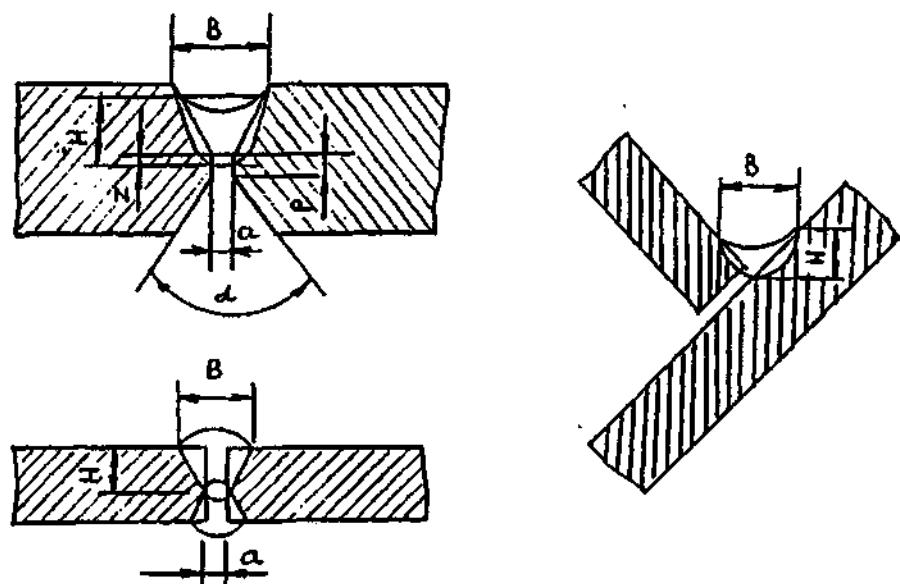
Геометрические параметры подготовки кромок и поперечного сечения шва:
